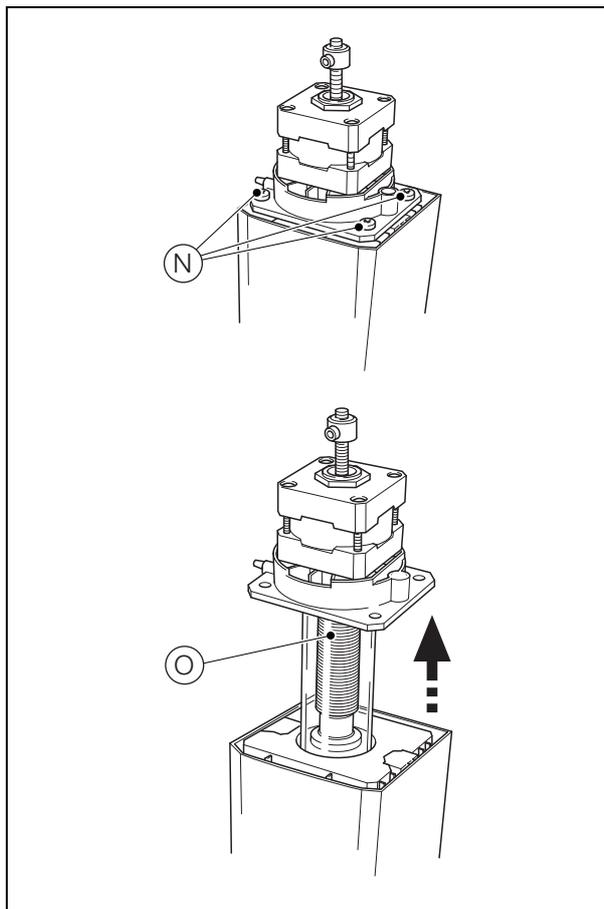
Desmontaje del motor y del tubo de muestra
